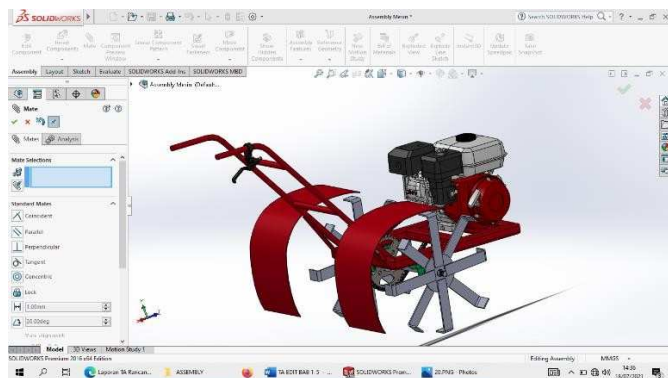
161 Hasil Assembly Bolt dan Poros Roda
